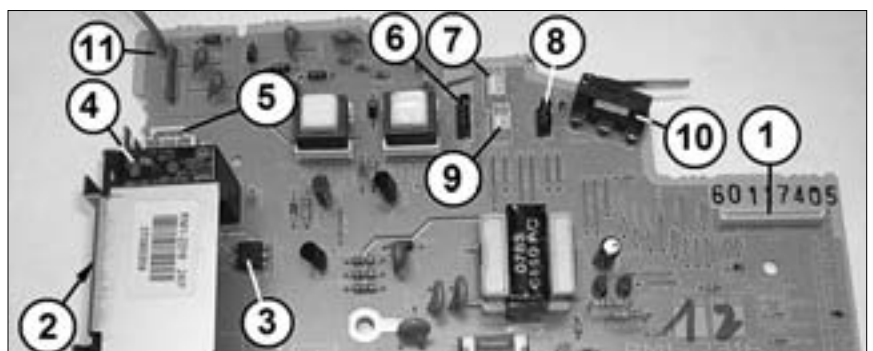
Часть 2 платы Power supply PCB, вид сверху
